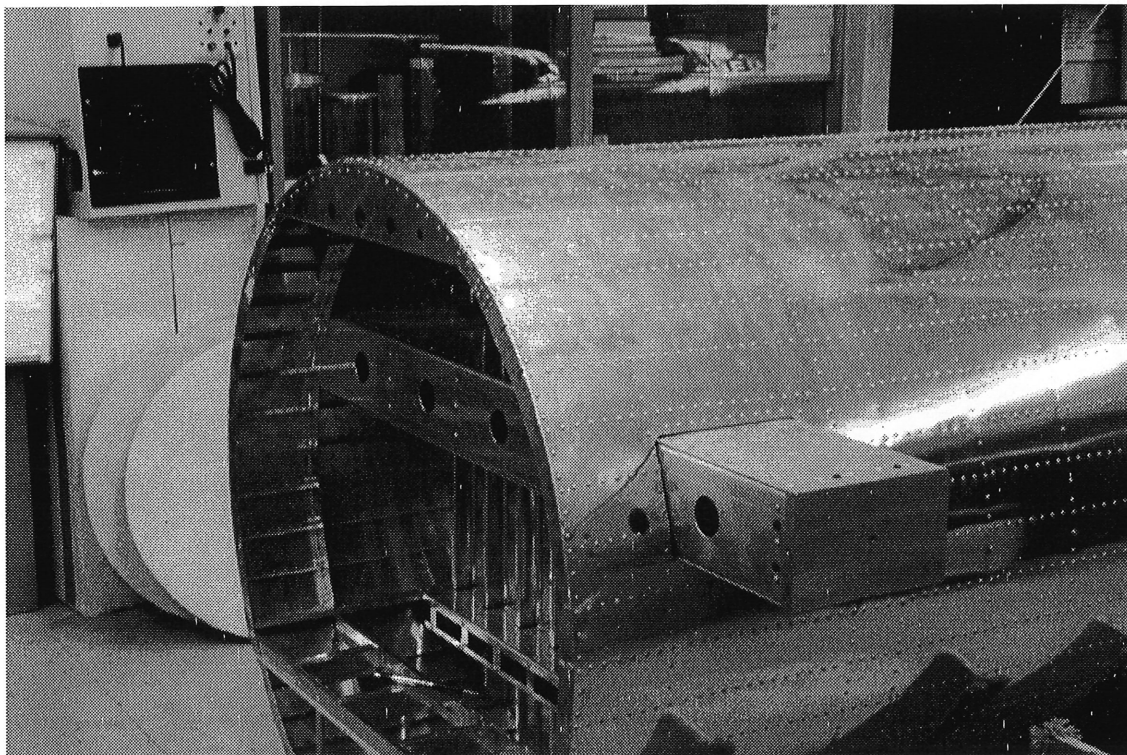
Vue arrière de la maquette (plaque et support moteur)
